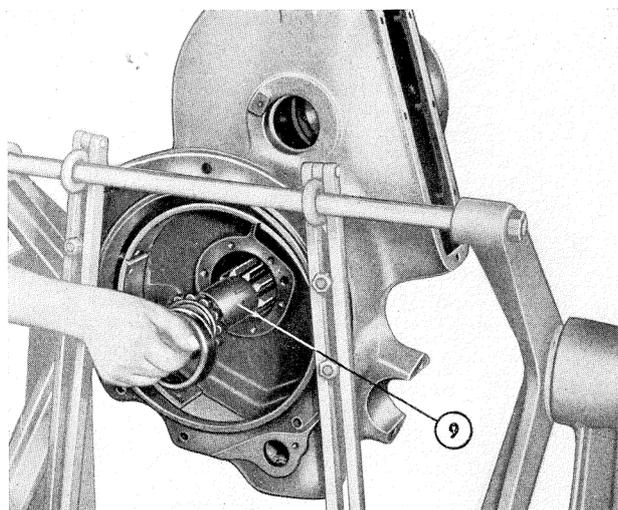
Démontage de l'arbre avec pignon conducteur (9) du carter de réducteur latéral.
